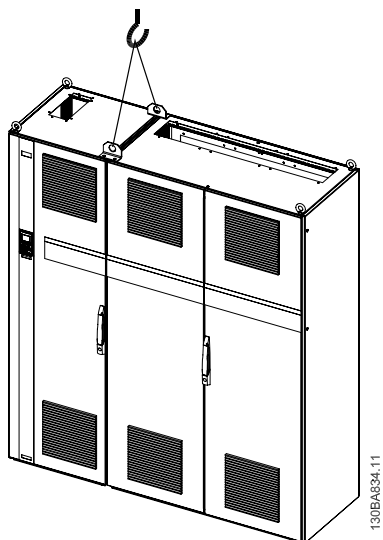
Рекомендуемый метод подъема, размер корпуса F2.
